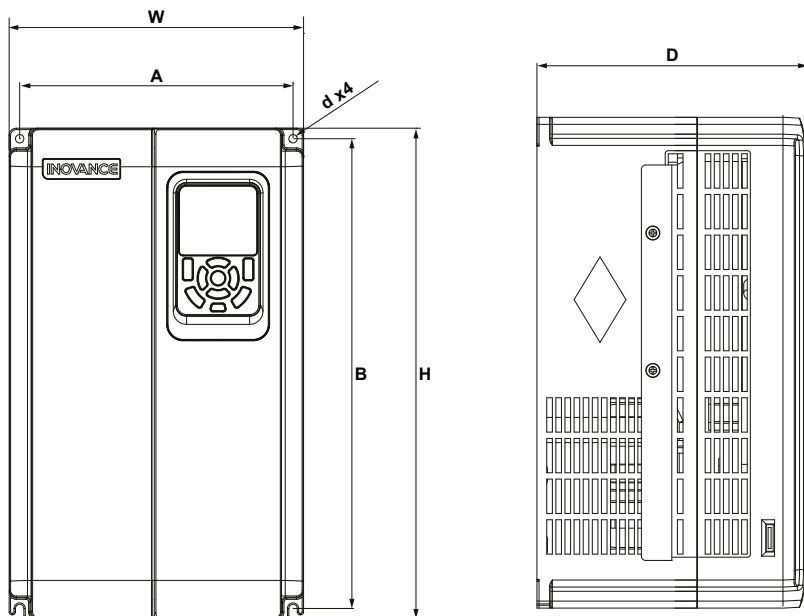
Внешний вид типоразмеров T5 - T6
